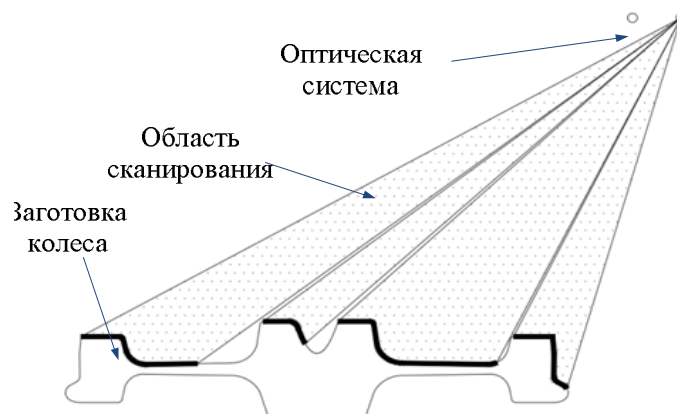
Полученный разрез заготовки колеса при смещении оси сканирования на 6°
